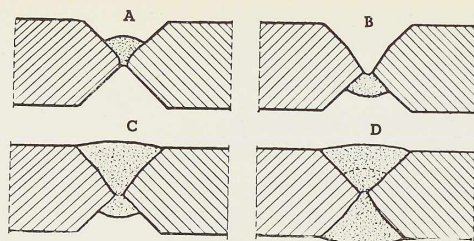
Mode opératoire préconisé en Allemagne pour les soudures bout à bout de forte épaisseur.
